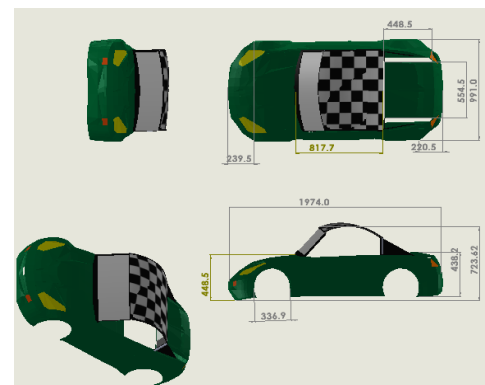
Planos del diseño e isométrico con dimensiones en mm.
